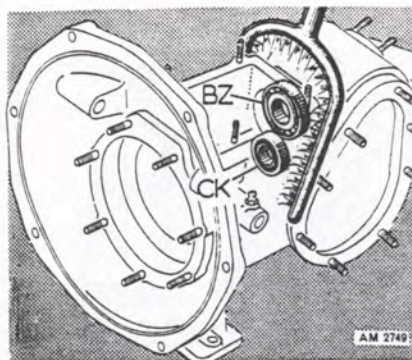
Um die Getriebelager ausbauen zu können, ist das Gehäuse mit einem großen Schweiß- oder gabelförmigen Gasbrenner in der gezeigten Art zu wärmen.
